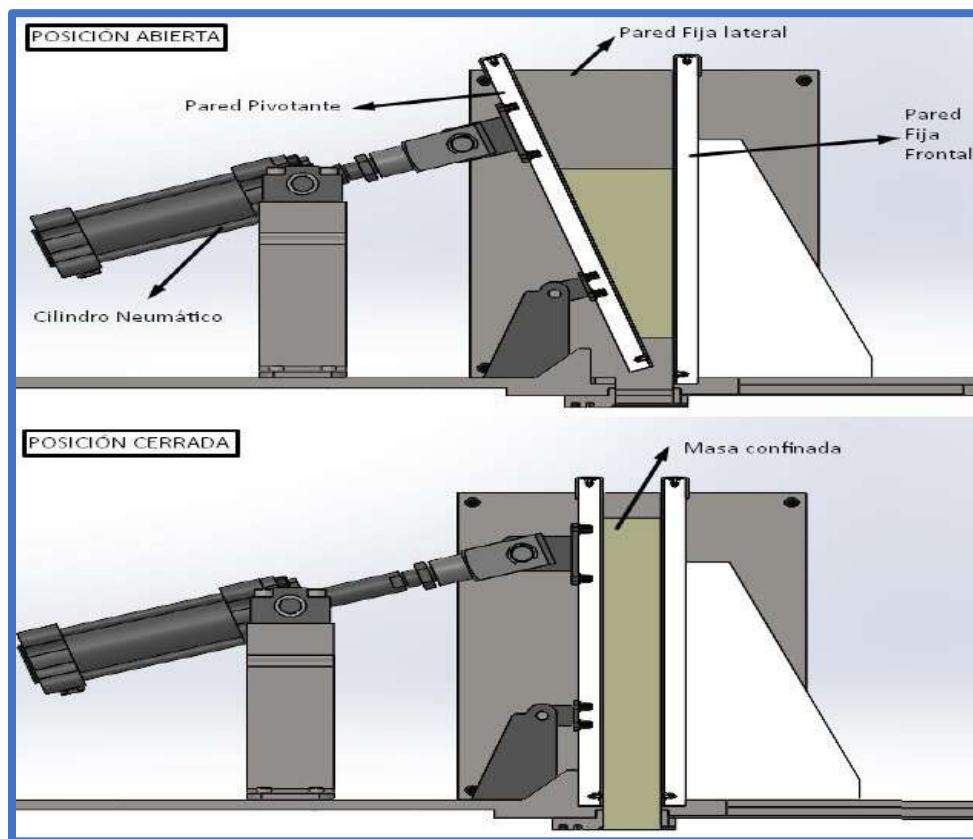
Posición abierta de la “Pared Pivoteante” (Imagen Sup) – Posición cerrada de la “Pared Pivoteante” (Imagen Inf)
